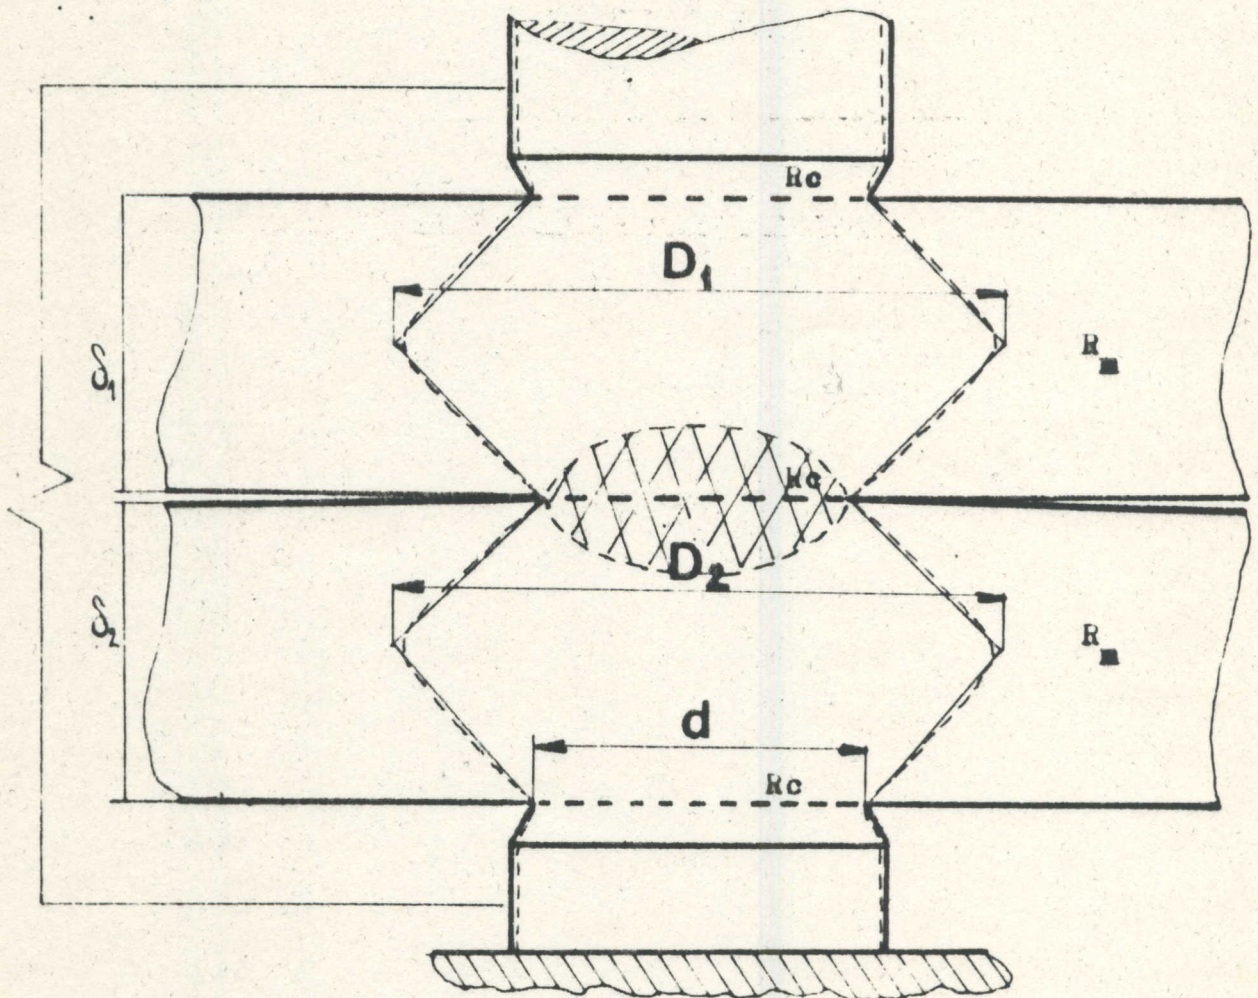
Schéma de la zone de soudage.
